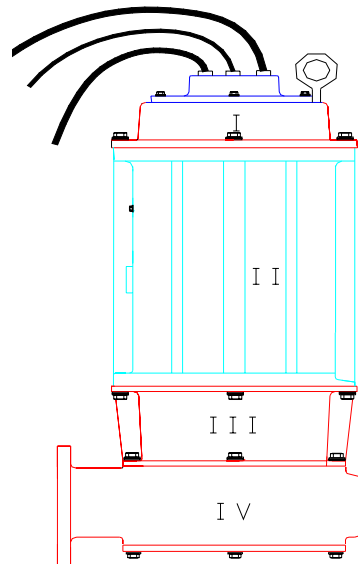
↑ Elementos principales de una bomba AFP accionada con un motor FRAME 250.
